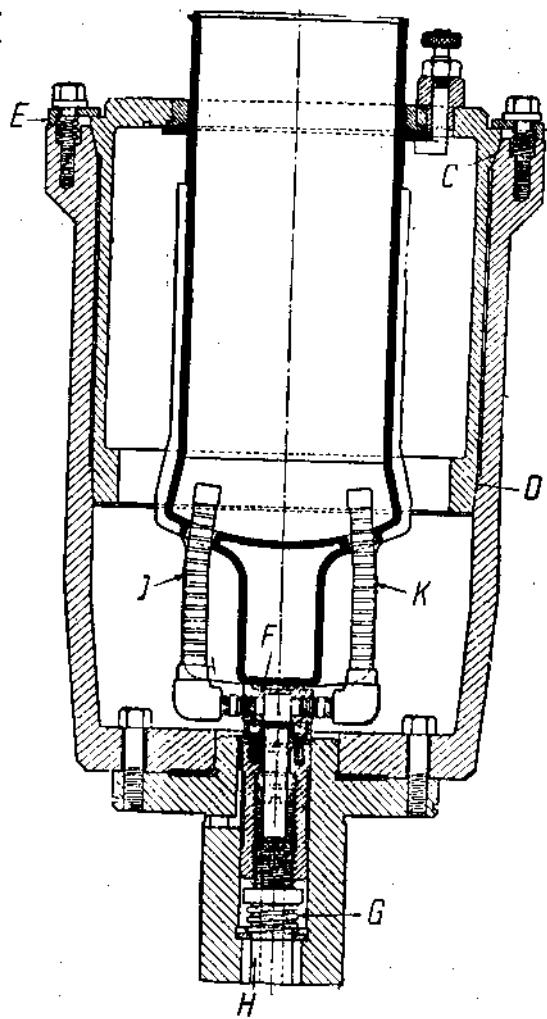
Приспособление для шлифовки цилиндра аэропланного мотора
